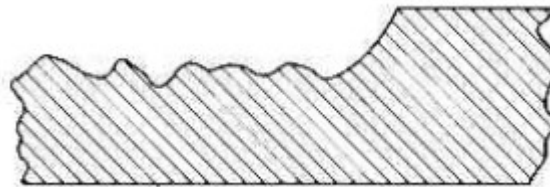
Defeito por aparecimento de canal devido a bolhas de gás [59]
